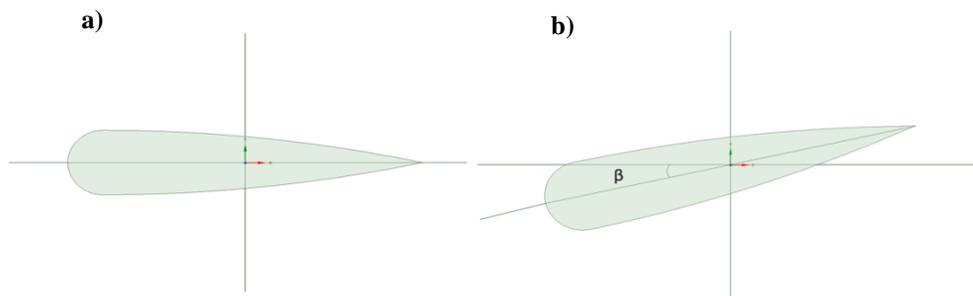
Alabes de picoturbina; a) Vista de planta de los perfiles b) Variación de los ángulos. picoturbina
